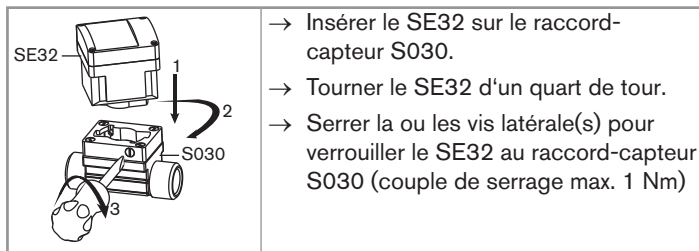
Assemblage du SE32 sur le raccord-capteur S030
